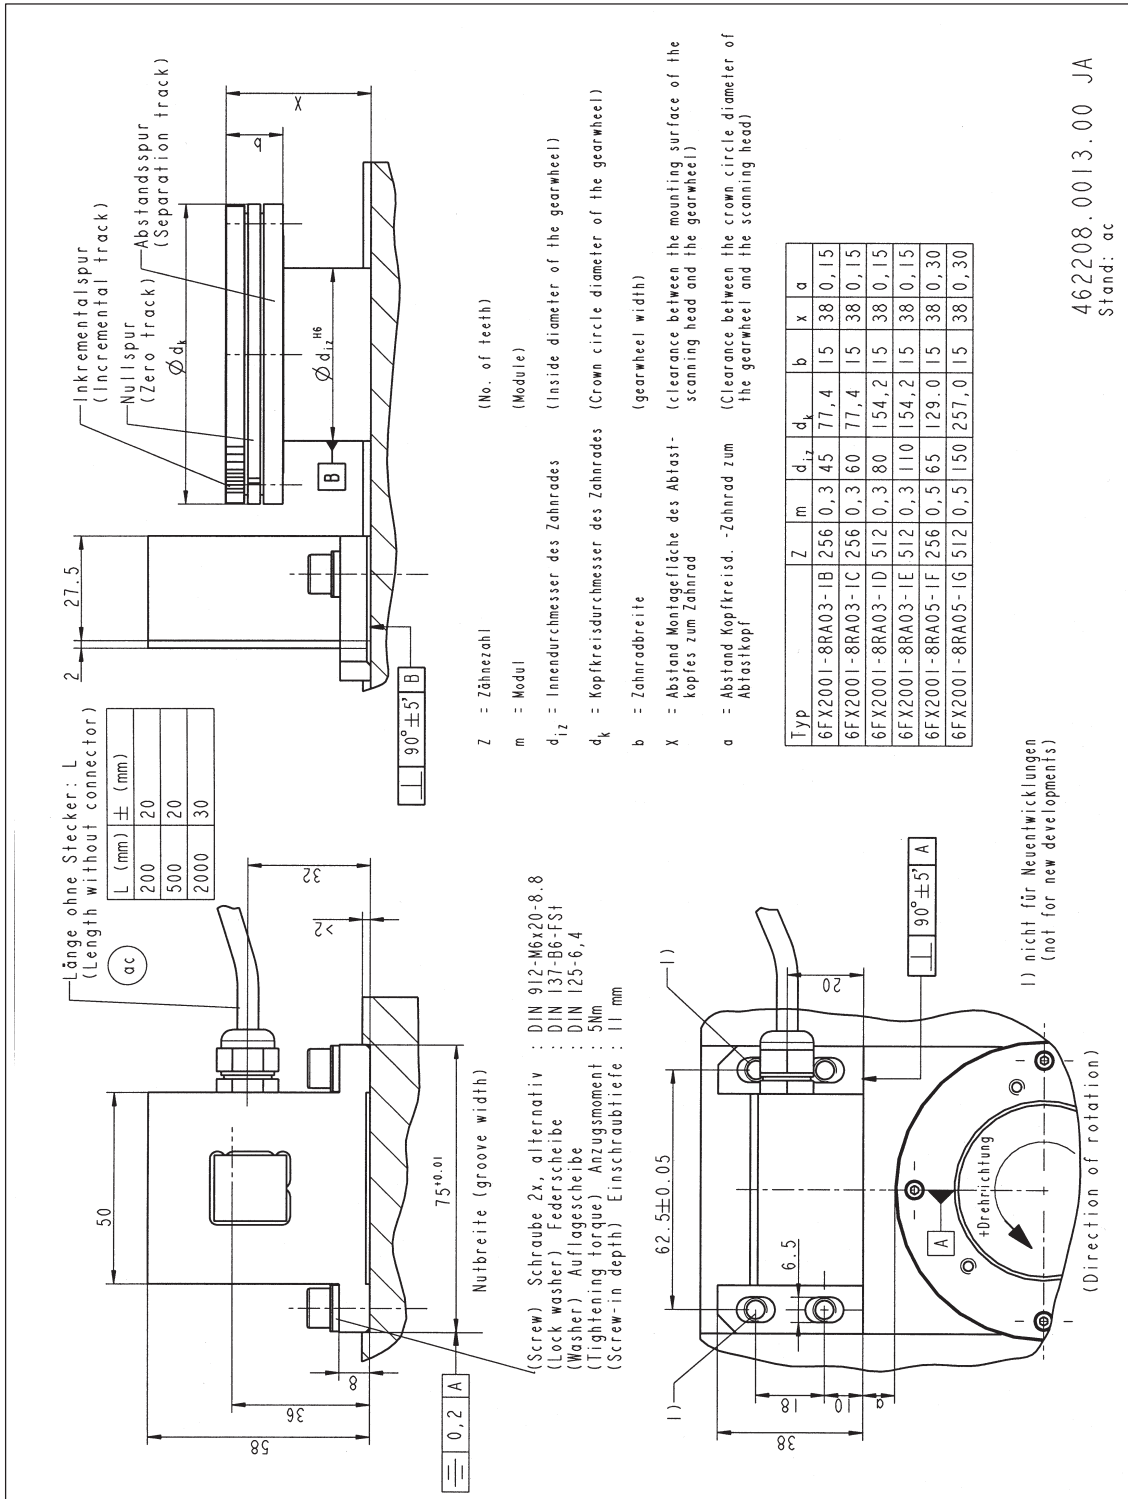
Montagezeichnung Zahnradgeber SIZAG 2
